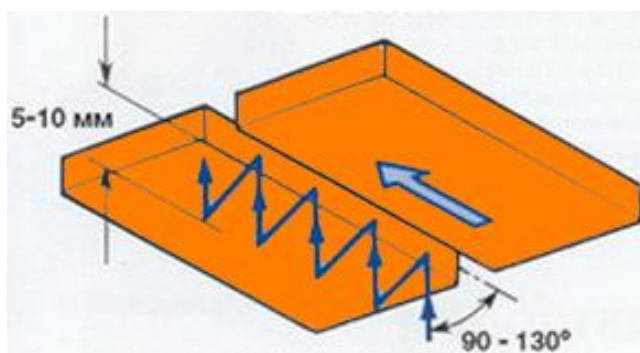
Тип шва С17- стыковой с разделкой кромок, сварка ручная дуговая ГОСТ 5264-80, положение шва – потолочное; толщина металла – 8 мм.
